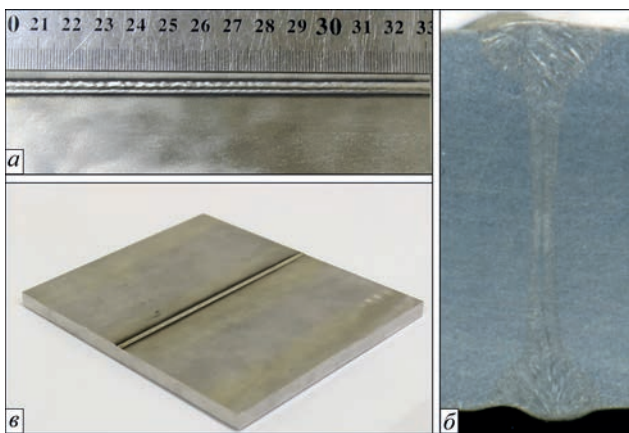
Двопрхідне гібридне зварювання пластин AISI304 ($\delta = 10$ мм): а – зовнішній вигляд шва; б – поперечний перетин; в – зовнішній вигляд зварного з'єднання
